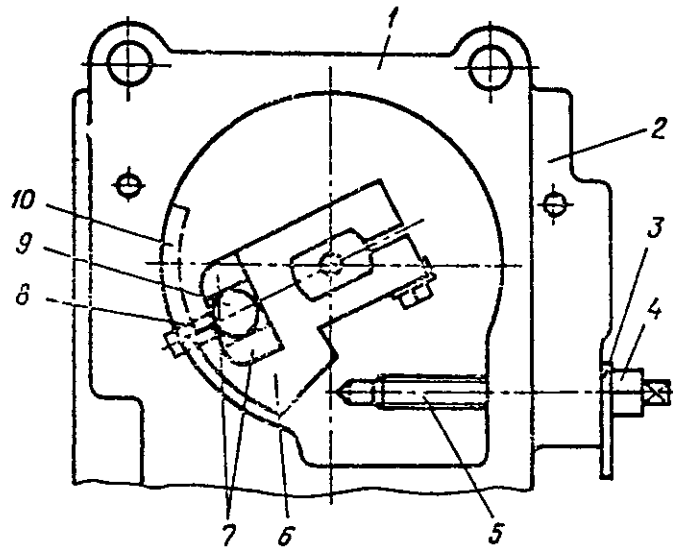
Исполнительный механизм ИМ-24А (вид со стороны установочного фланца):
